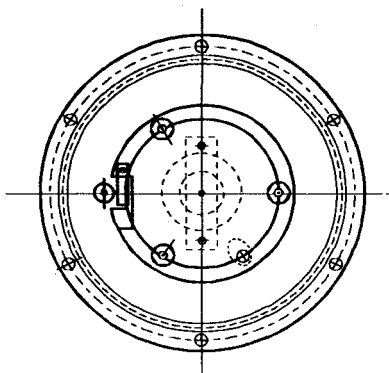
Croquis para la construcción de un contador de avalancha de placas paralelas
